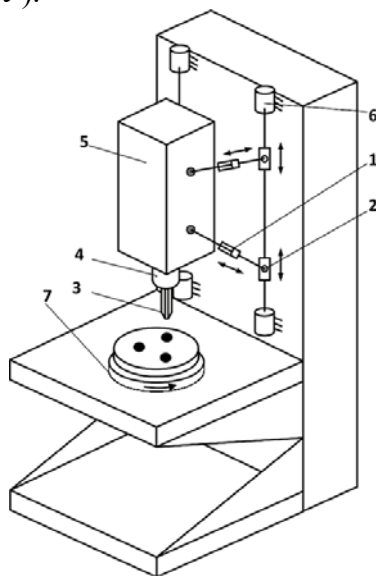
Компоновка резбонарезного станка с комбинированным МПС
